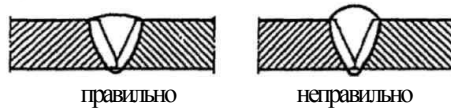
26. Превышение усиления сварного шва
